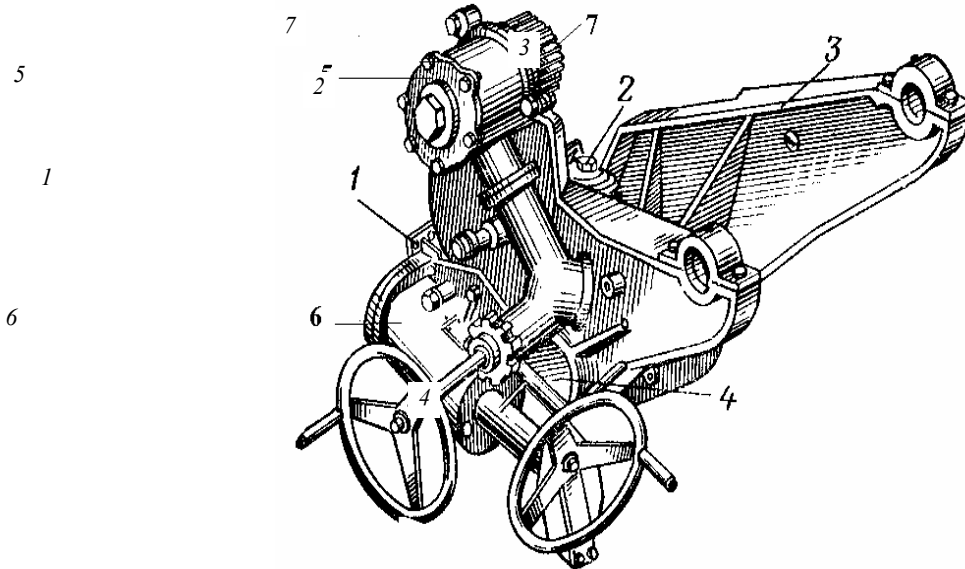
Верхний станок 122 мм гаубицы Д-30:
